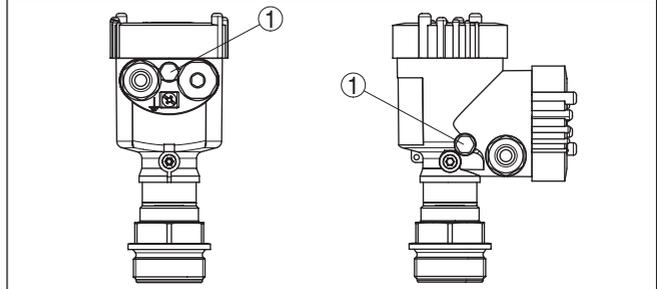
Posição do elemento de filtragem - Passagem hermética
